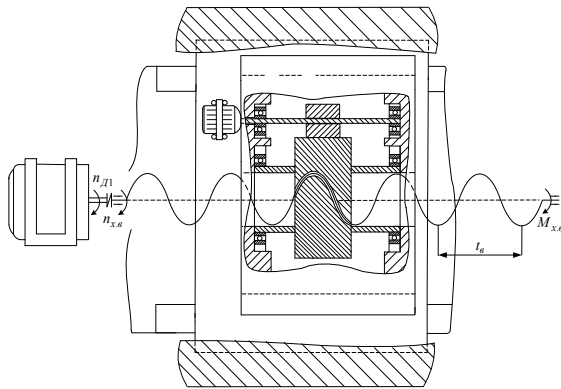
Вариант упрощенной схемы конструкции двухдвигательного безредукторного МП с ВХГ для подачи РО станка модели 24К60АФ4
